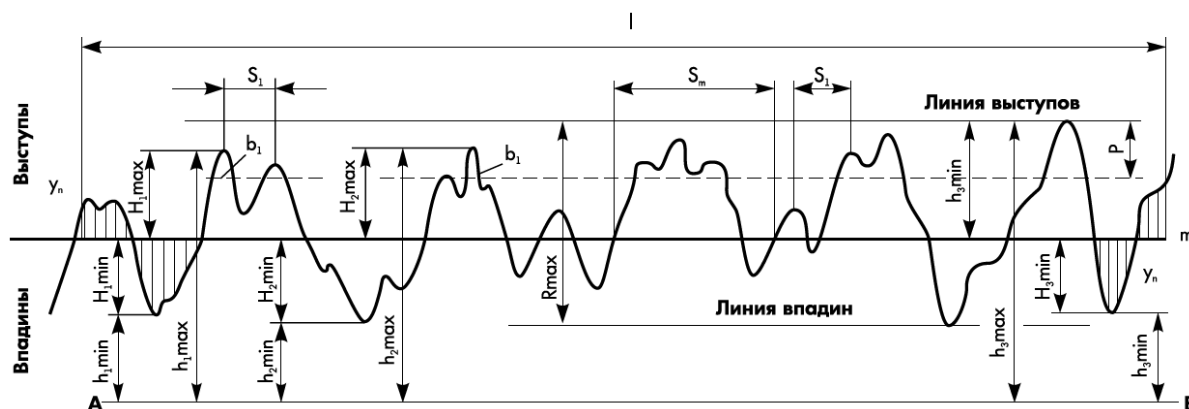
Схема шероховатости поверхности и ее элементы
